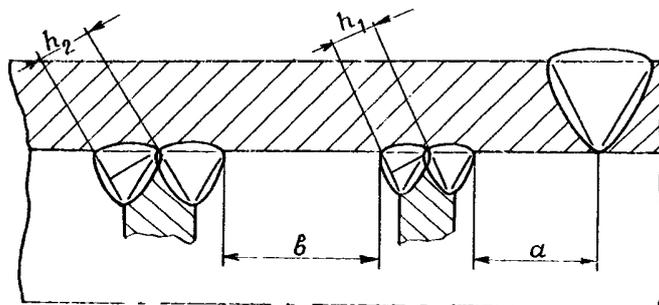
Расположение сварных соединений приварки деталей к поверхностям оборудования и трубопроводов
